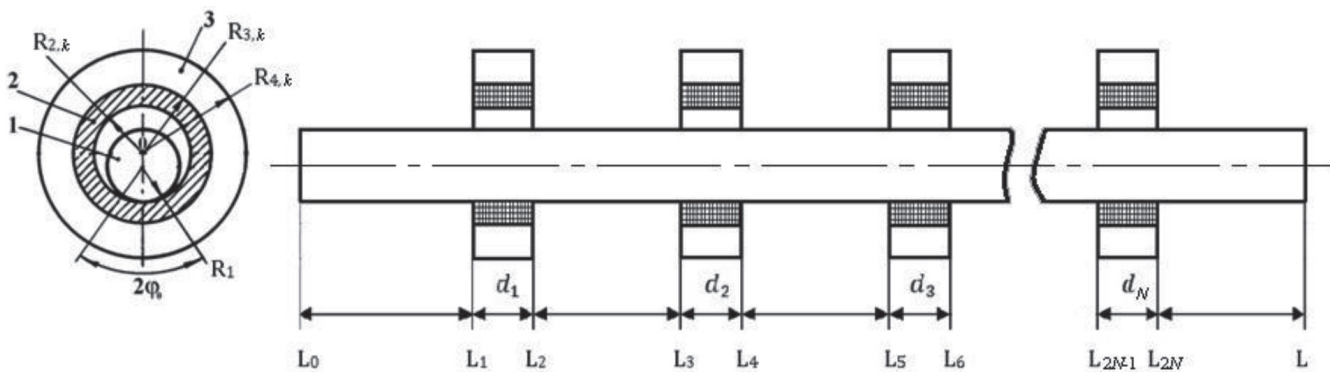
Модель системы подшипников скольжения: 1 – вал; 2 – втулка; 3 – корпус
